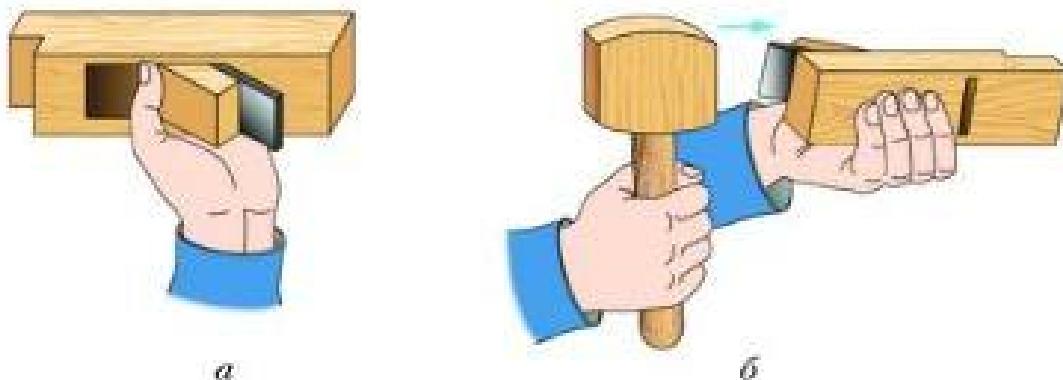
Извлечение ножа из рубанка с деревянной колодкой: *а* – захват рубанка; *б* – выбивание ножа
